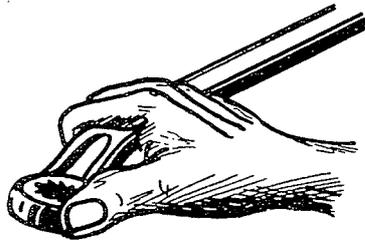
Handfest-Anziehen von Dehnschrauben mit Ringschlüssel mit Steckschlüssel
